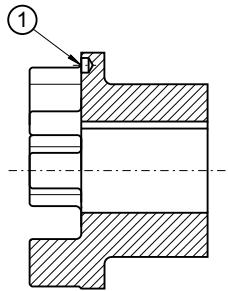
Position der Ausgleichsbohrung beim Ein-Ebenen-Auswuchten
